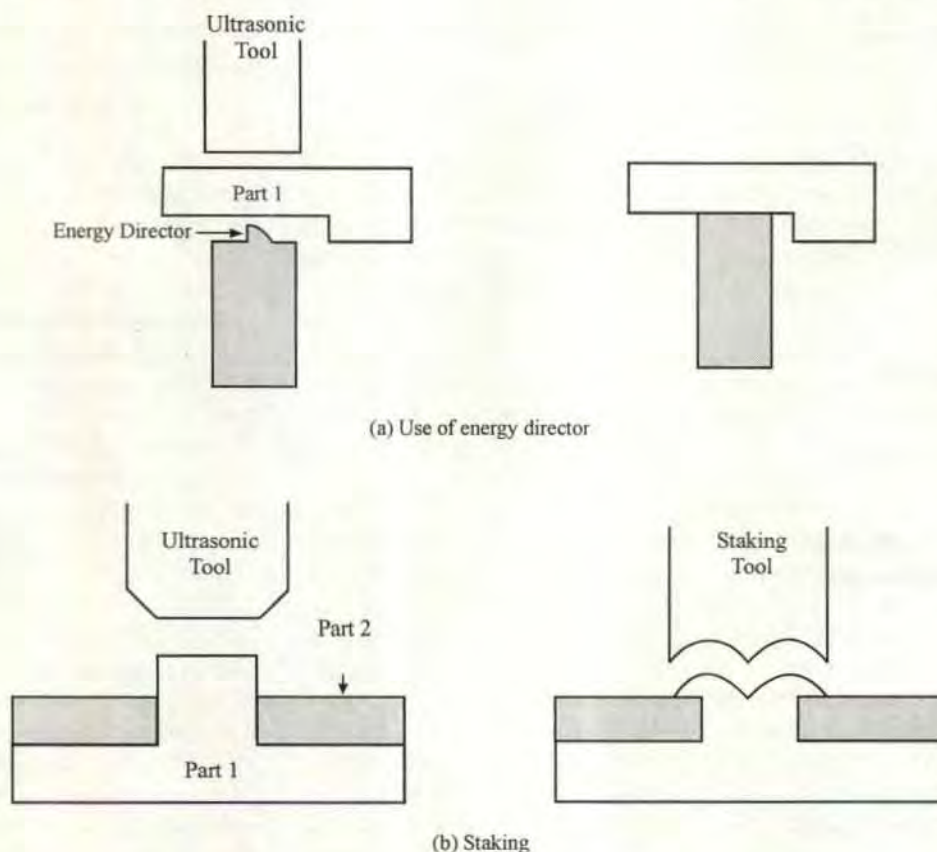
Soldadura ultrasónica que muestra (a) el uso de un director de energía para obtener una soldadura ultrasónica eficiente y (b) el principio de piqueteo
